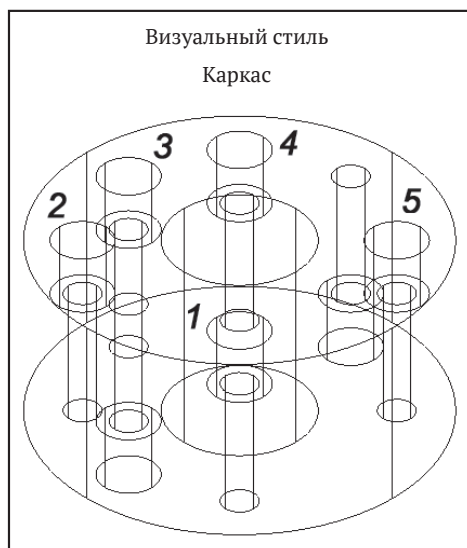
Построение пяти ступенчатых отверстий в промежуточном виде 3D-модели детали «Корпус»
